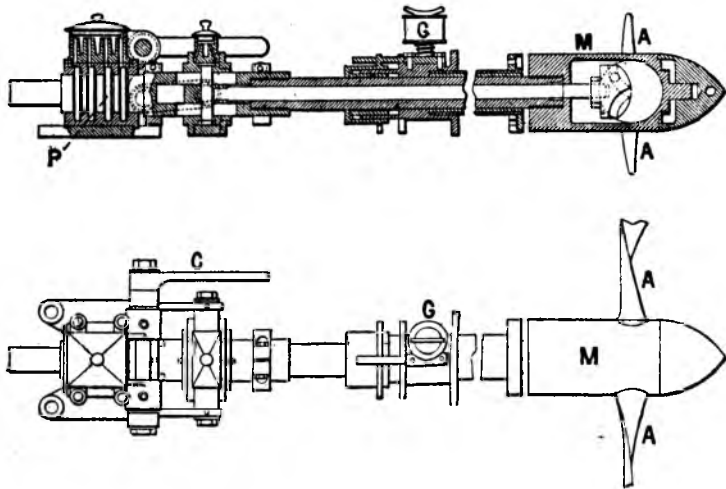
Винт с поворотными лопастями *А* и гребной вал с приспособлениями для поворота лопастей. — *М*, втулка винта, заключающая механизм для поворота лопастей. — *Р*, упорный кольцевой подшипник. Кольца расположены в ряд для распределения давления. — *Г*, штауфер для смазки направляющего сплошного подшипника. — *С*, рычаг для поворота лопастей.
